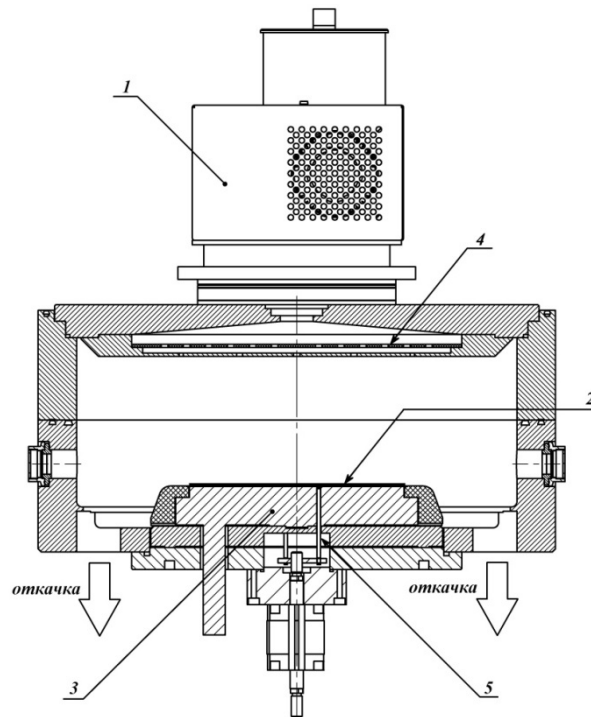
Конструкция реактора установки с СВЧ источником для очистки пластин.
